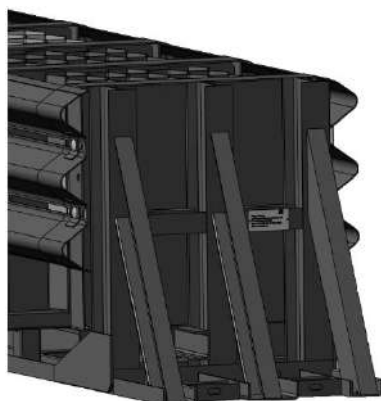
Расположение маркировочной бирки на ФО-Д(М)-У2-П-110-5,87
